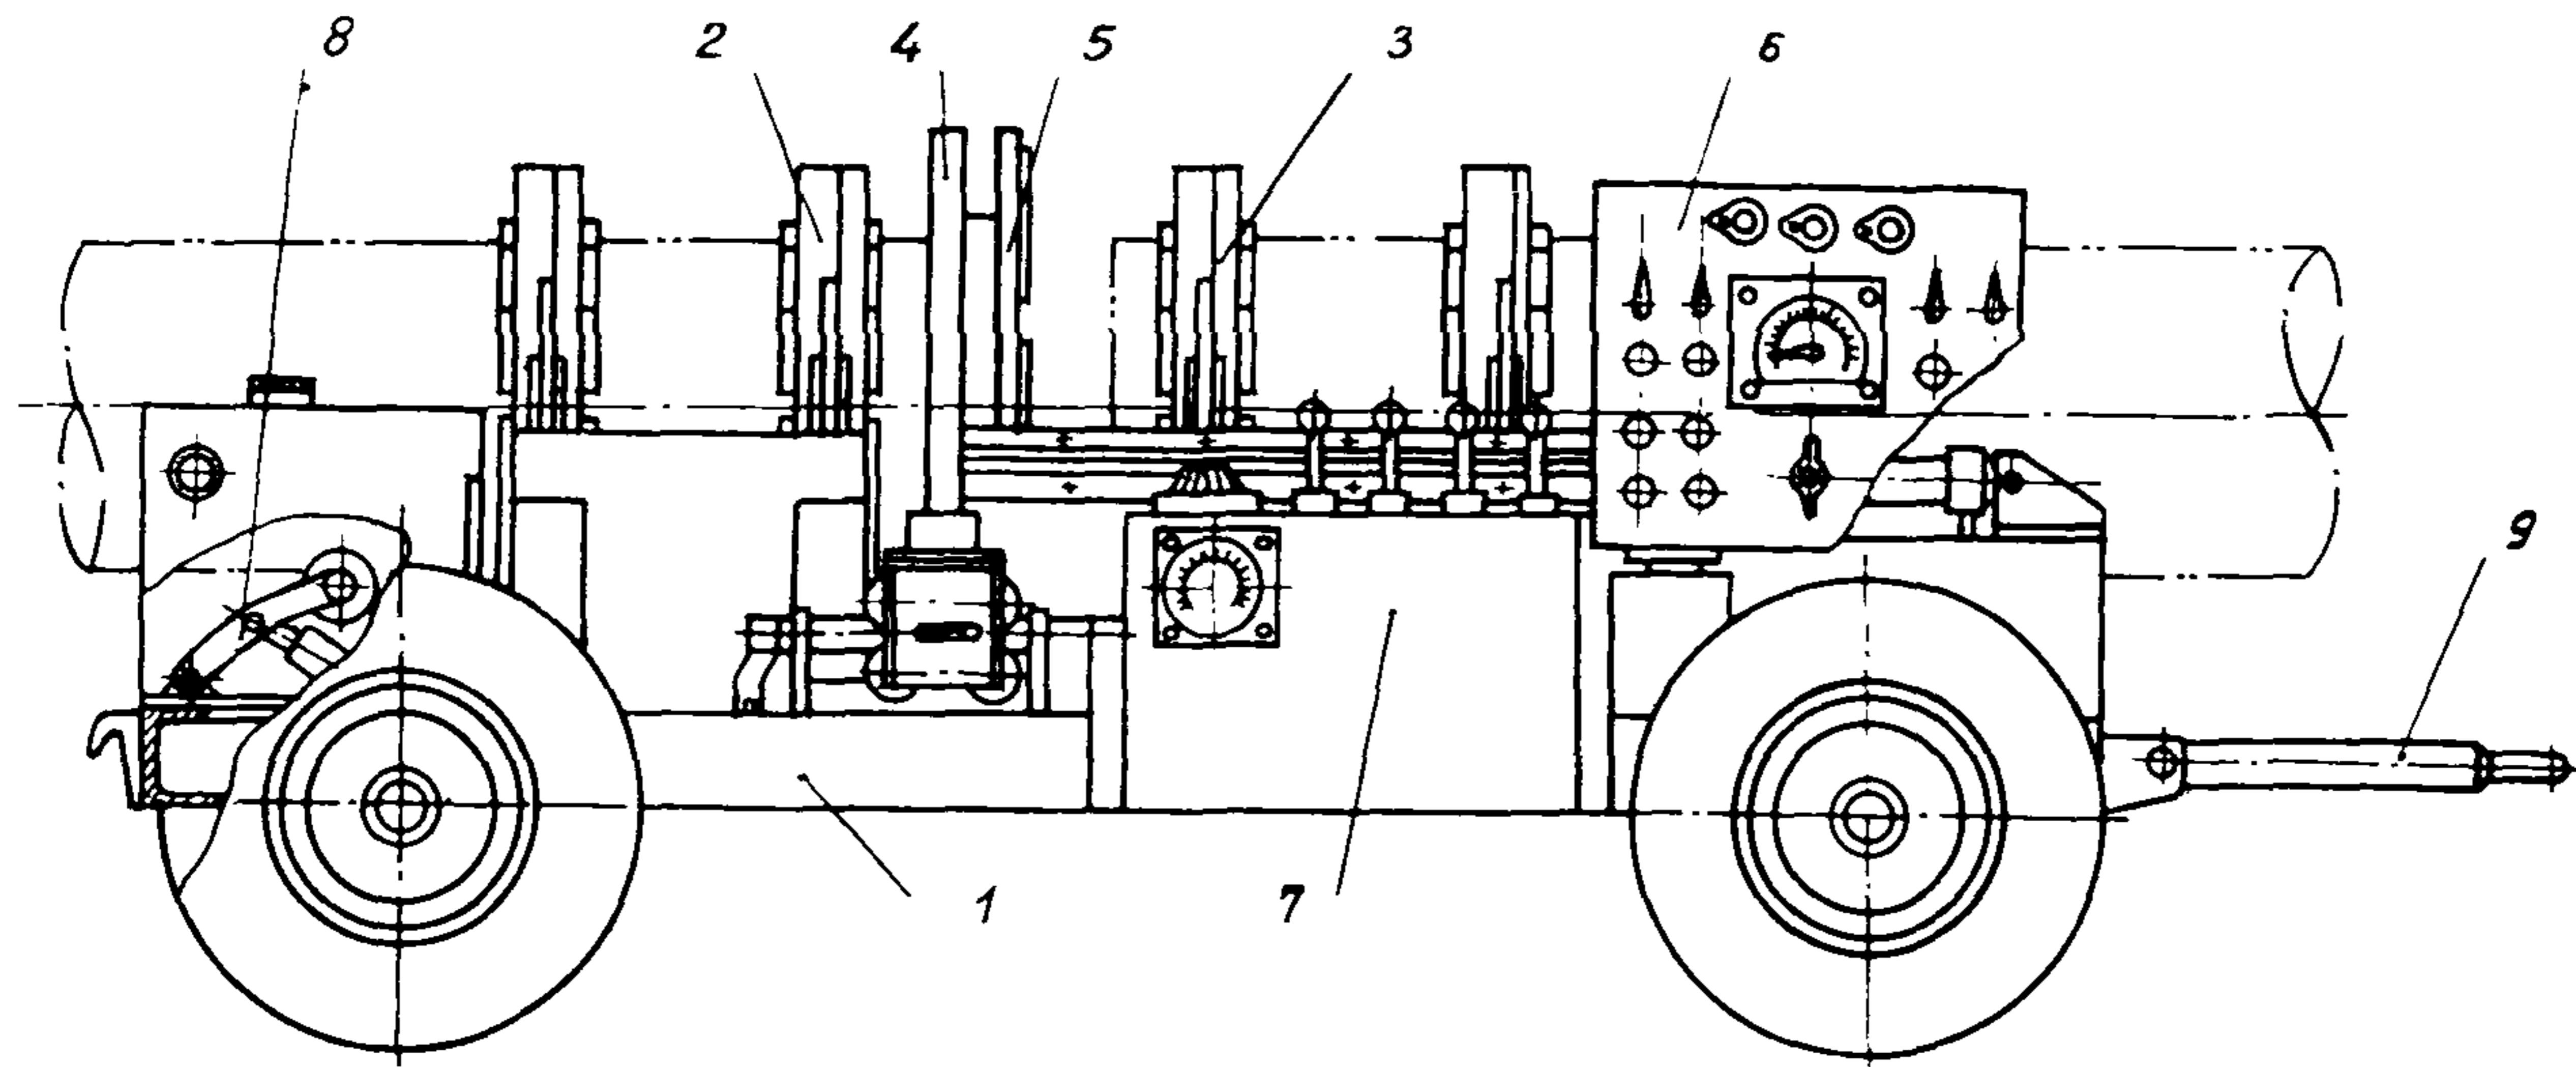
Схема установки УСПТ-7 для контактной тепловой сварки встык пластмассовых труб диаметром 140-355 мм:
